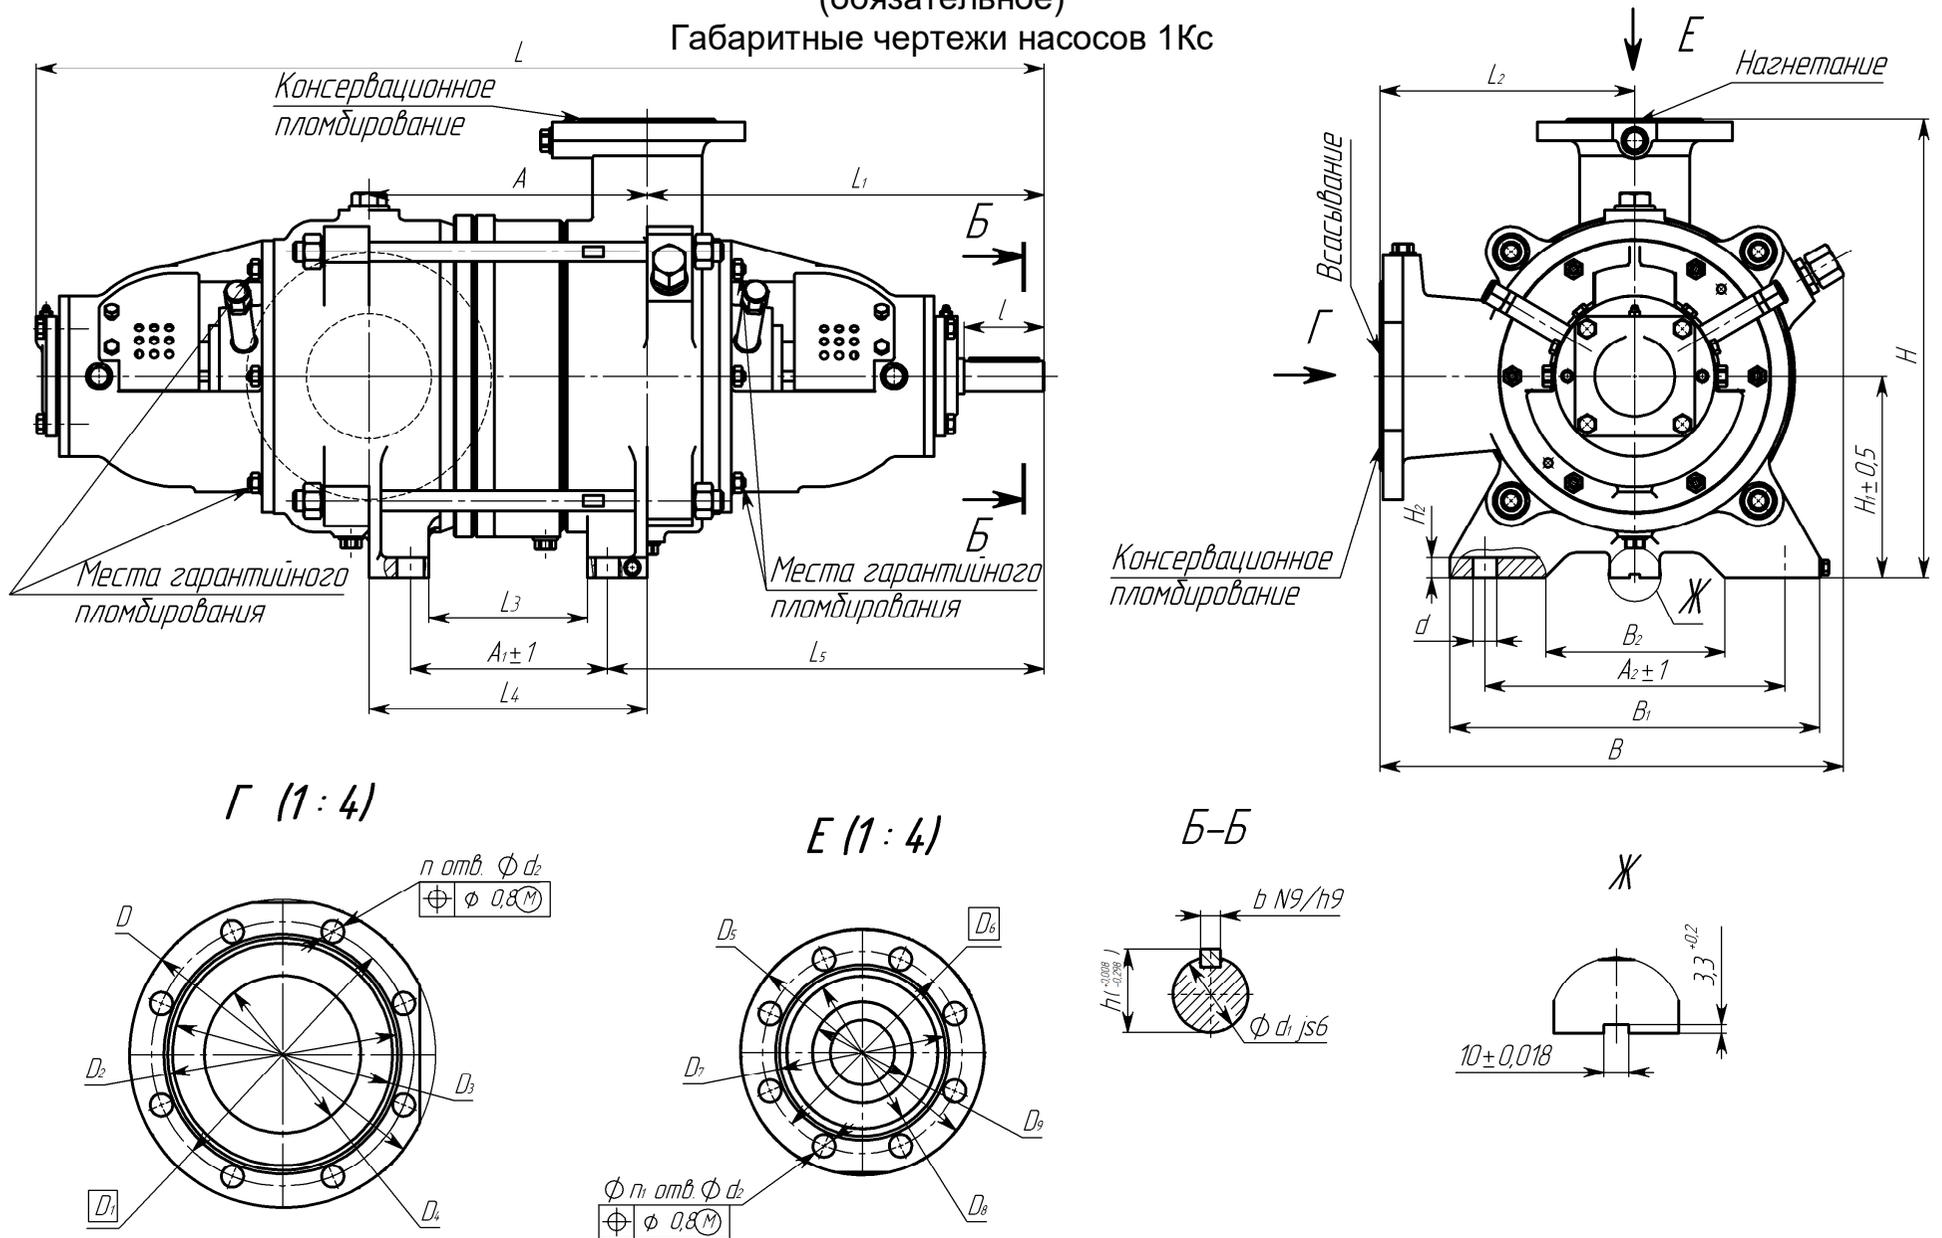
Габаритный чертеж насосов 1Кс32, 1Кс50, 1Кс80
